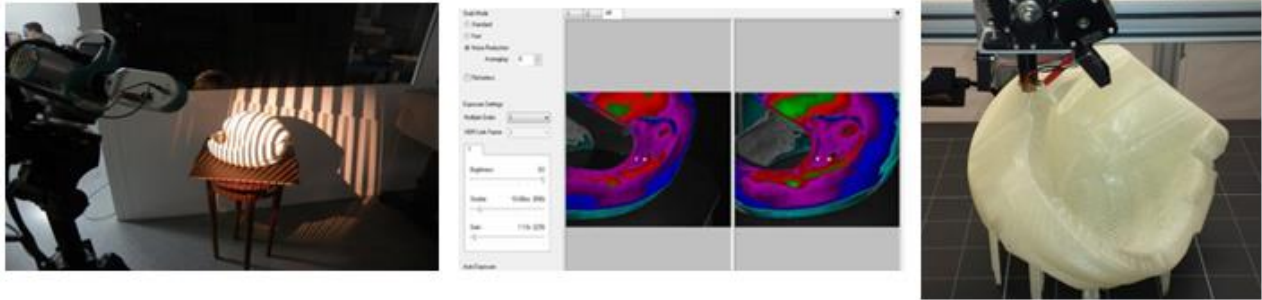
Ingeniería inversa sobre un casco. De izquierda a derecha: escáner 3D, rediseño e impresión 3D.
